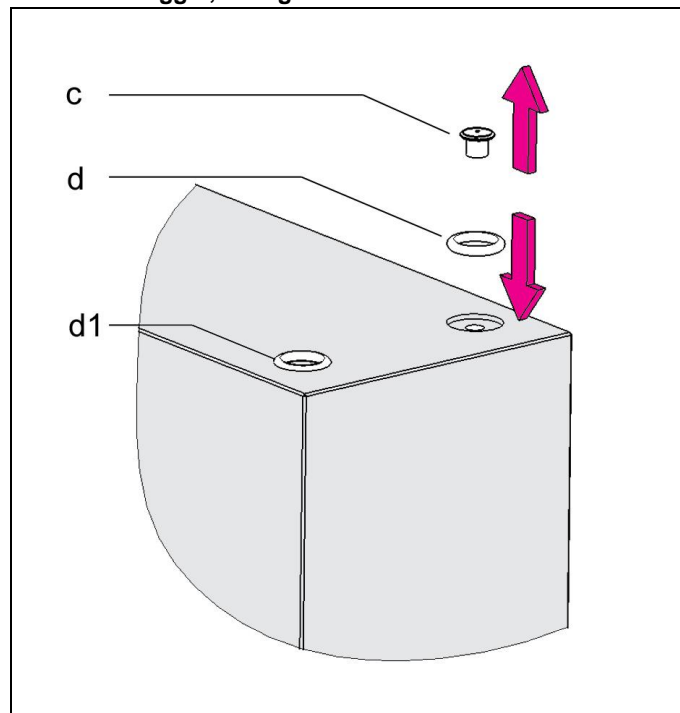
Esempio, installazione della versione a flangia (senza tubi)
